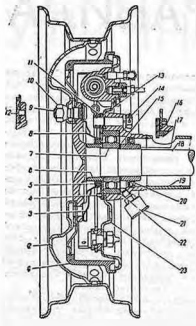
Крепление заднего колеса и полуси. 1 — тормозной барабан, 2 — диск колеса, 3 — маслоотражатель наружный, 4 — винт крепления корпуса сальника, 5 — войлочный сальник, 6 — штука сальника, 7 — подшипник полуси, 8 — маслоотражатель внутренний, 9 — болт, 10 — гайка, 11 — корпус сальника, 12 — винт крепления тормозного барабана, 13 — пластина крепления подшипника, 14 — болт крепления подшипника полуси, 15 — пружинная шайба, 16 — винт крепления тормозного щита, 17 — запорное кольцо подшипника, 18 — полуси, 19 — кожух полуси, 20 — резиновый сальник, 21 — маслянка, 22 — пружинная прокладка, 23 — тормозной щит.
